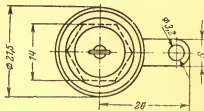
Габаритный чертеж диодов Д242 — Д244БП.
